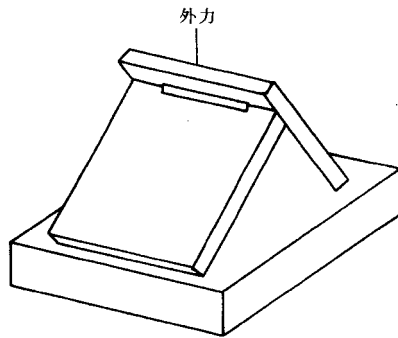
定位焊考试试件断裂试验方法示意
